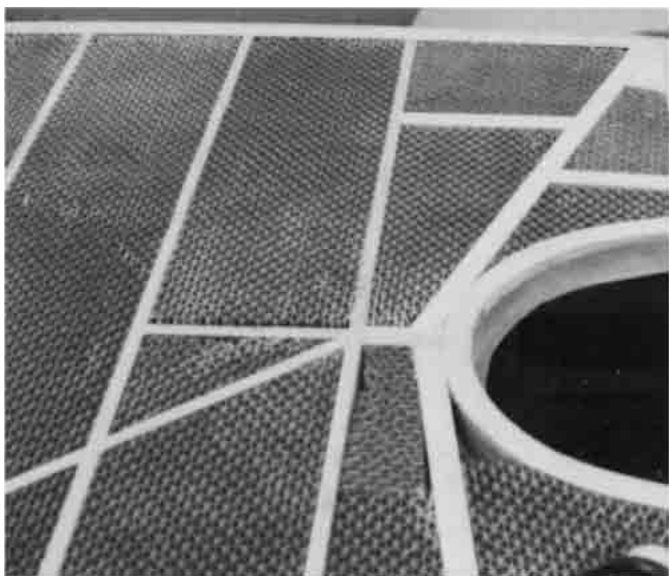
Decksconstruction mit leichten Wabenkern-Platten. Siehe Kap. 25, in dem diese Bauweise eines Decks ausführlich beschrieben wird.
